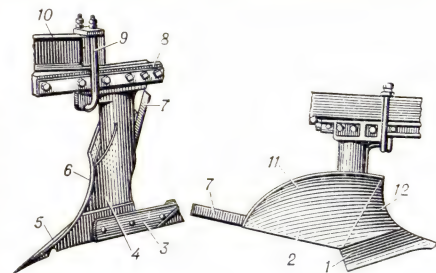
Корпус плуга: 1 — лемех; 2 — отвал; 3 — полевая доска; 4 — стойка; 5 — полевой обрез лемеха; 6 — полевой обрез отвала; 7 — перо; 8 — рама плуга; 9 — скоба; 10 — брус жёсткости; 11 — крыло; 12 — грудь.
